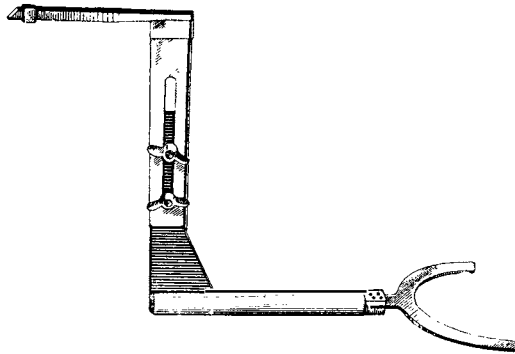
Приспособление 48001-1-125П для установки балансира под угол закручивания торсиона и определения остаточной деформации торсионов
